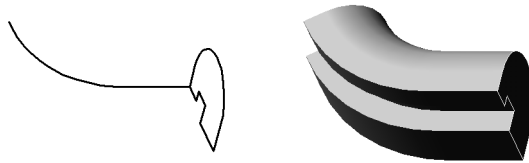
Эскизы и элемент, образованный кинематической операцией
